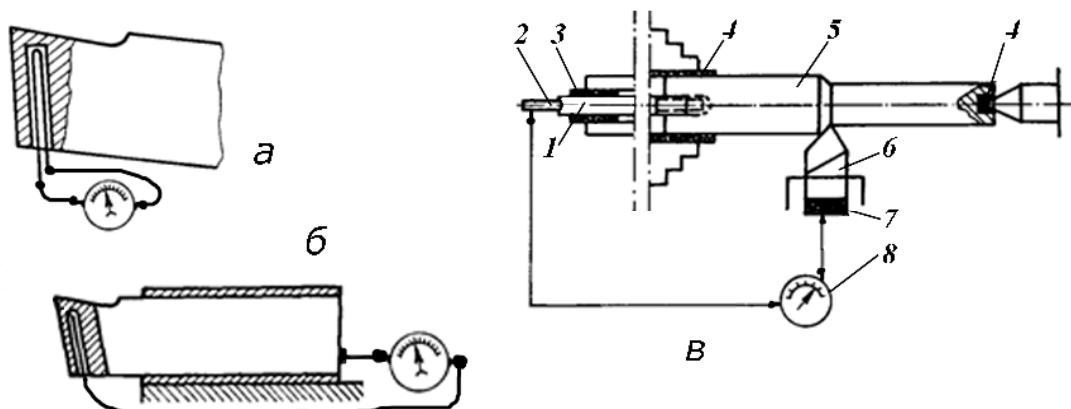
Схеми вимірювання температури різання за допомогою термопар: а – штучної; б – напівштучної; в – природної; 1 – рухомий контакт; 2 - нерухомий контакт; 3 – електроізоляційна втулка; 4 – електроізоляційні елементи; 5 – заготовка; 6 – різець; 7 – контактна група; 8 – вимірювальне обладнання
